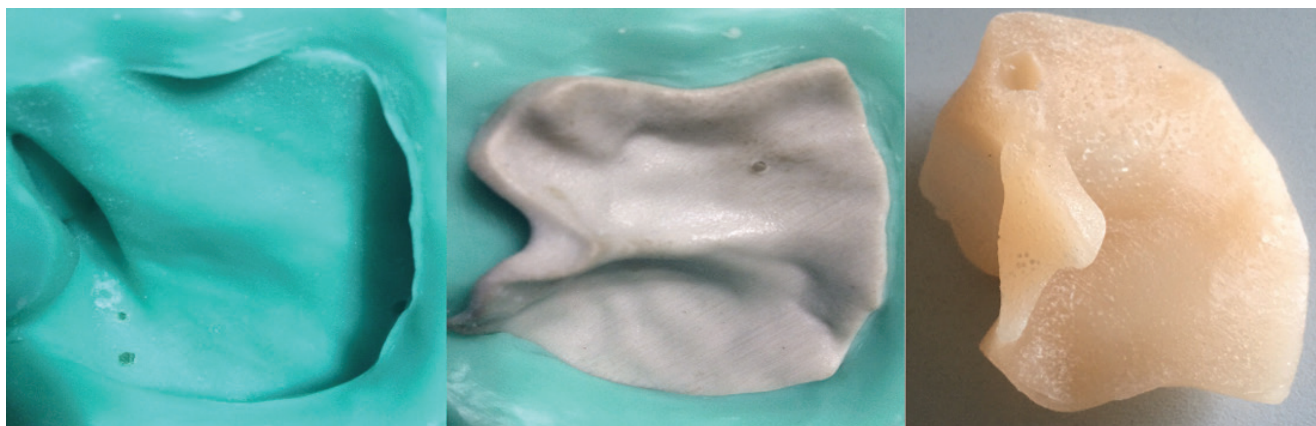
Изготовление пресс-формы из пластика на 3D принтере для изготовления имплантата
